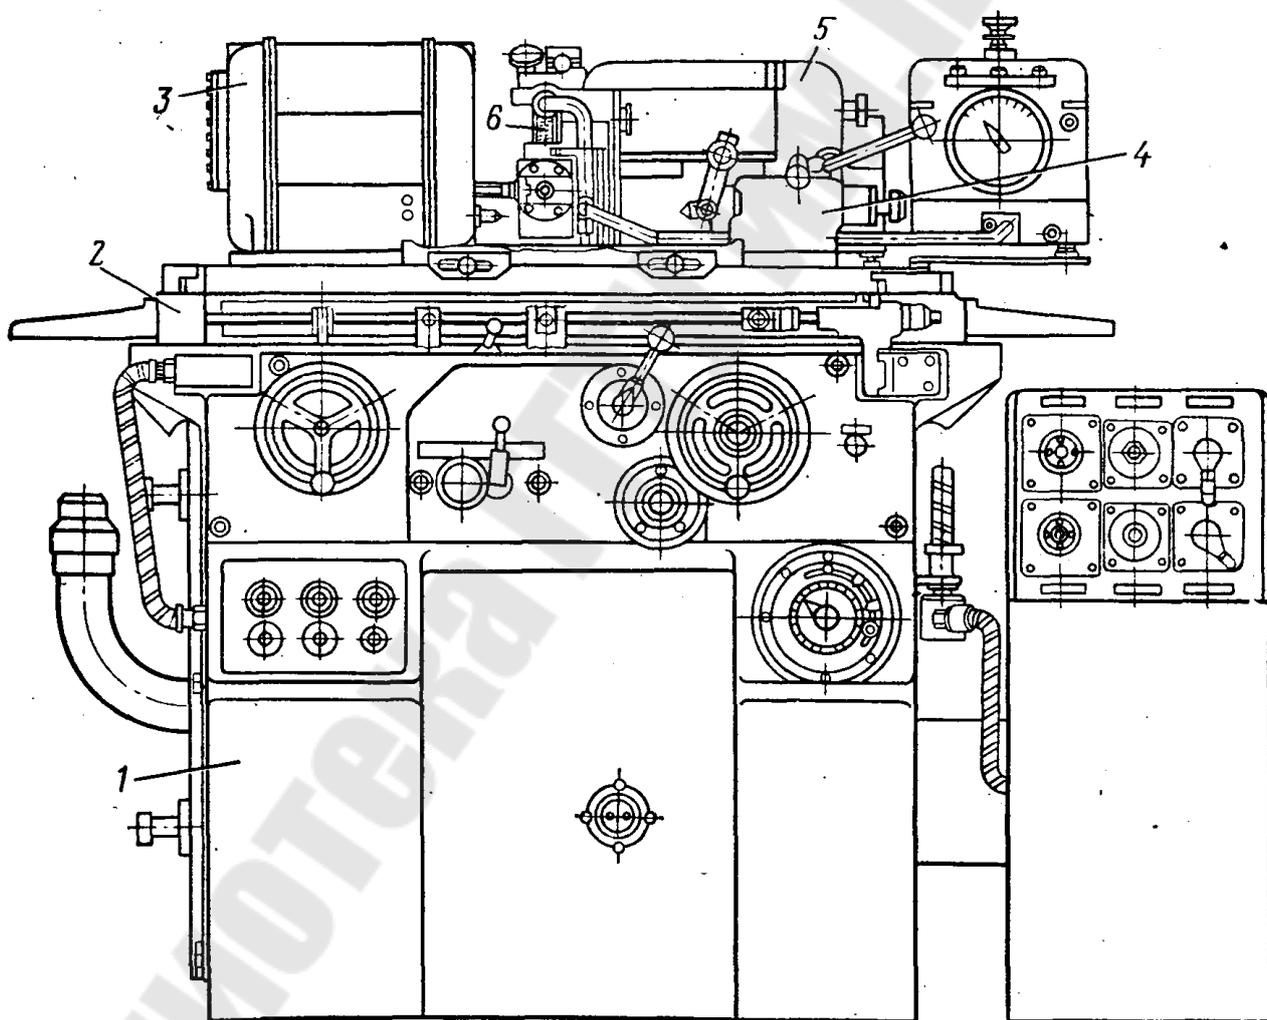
Общий вид круглошлифовального центрового станка
